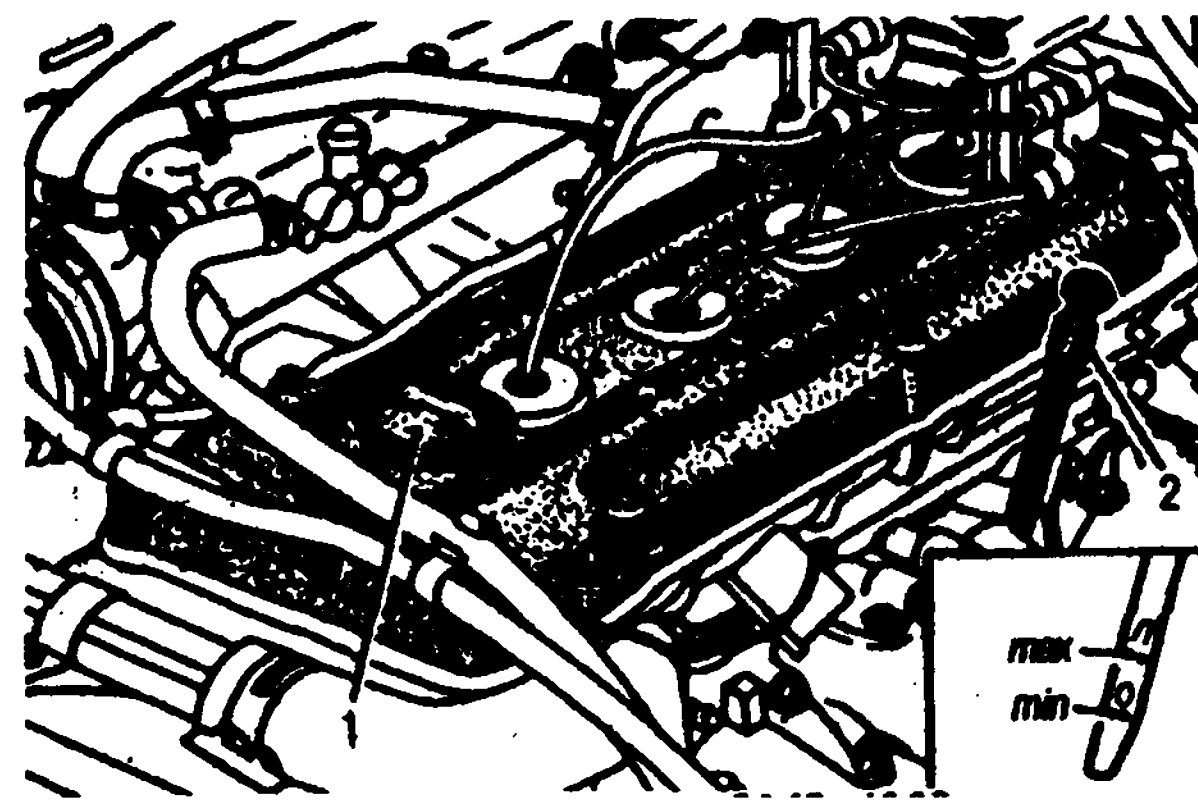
Двигатель ЗМЗ-4062: 1 - пробка маслозаливной горловины; 2 - масляный щуп
